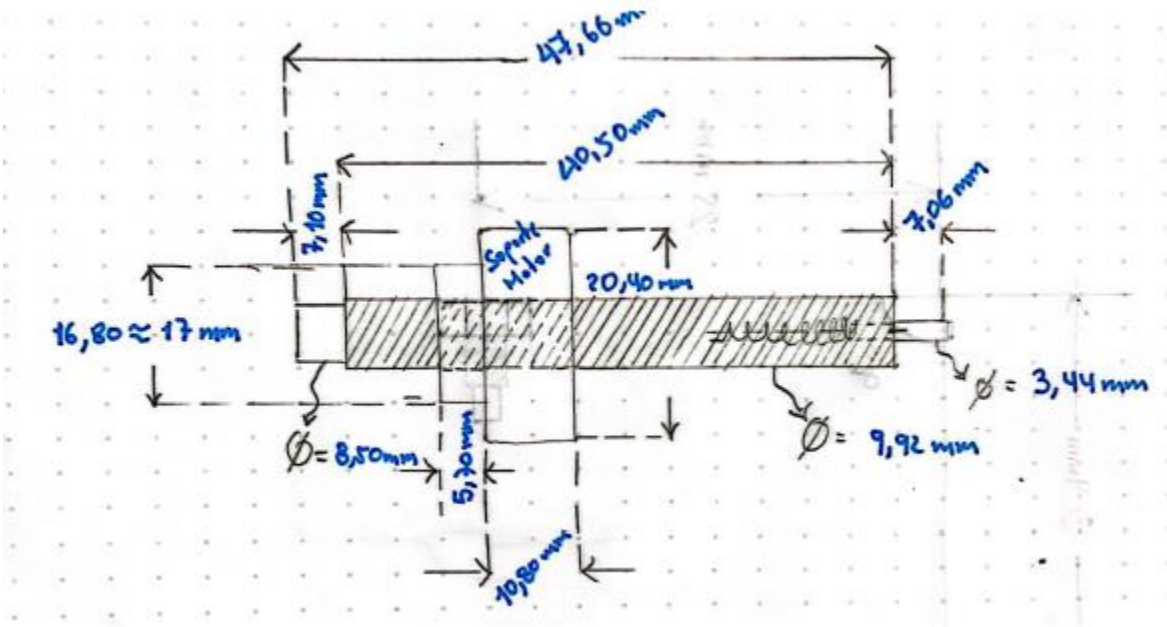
Dimensiones de tornillo de ajuste manual RPM motor a compresión.
